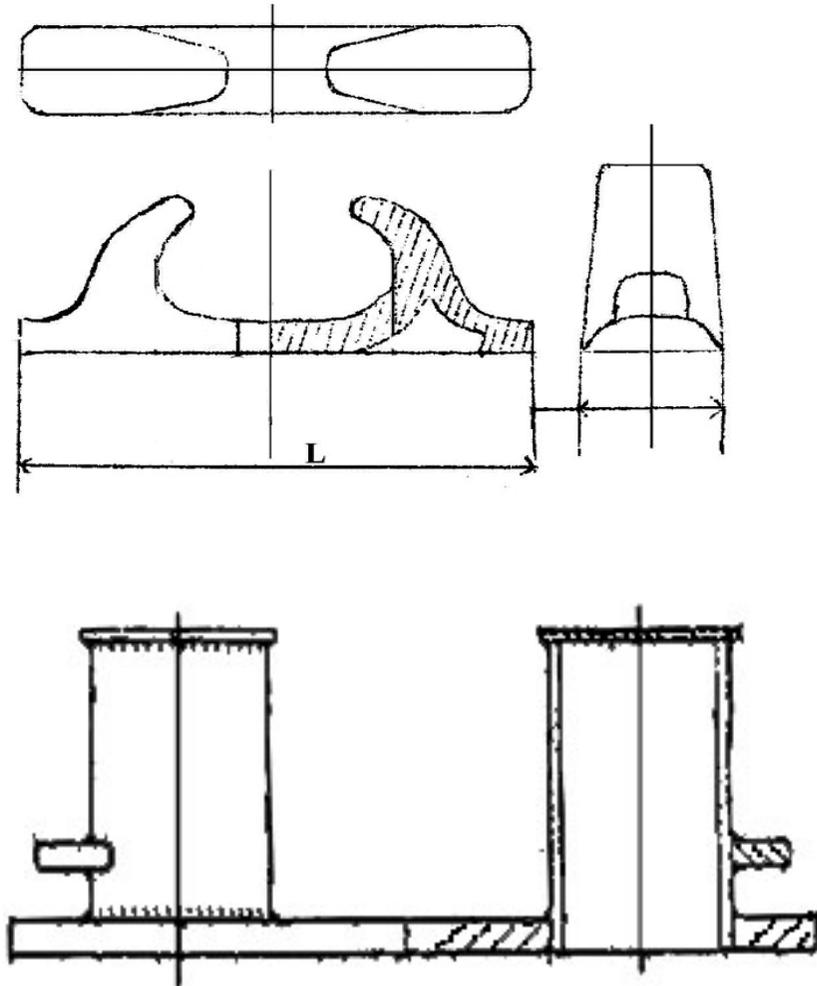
b. Bolder Membentuk Sudut (Miring) (Oblique Type Bollard)
